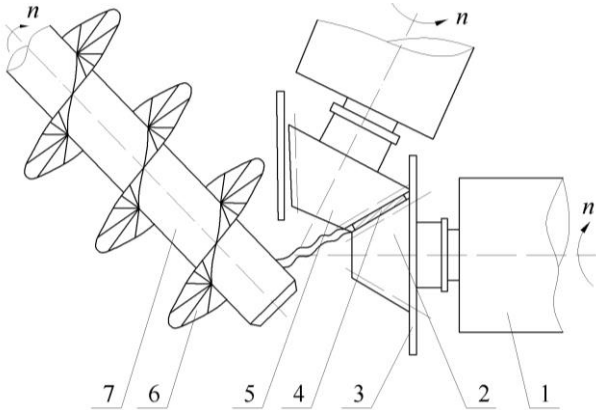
Схема формоутворення ГЗ парою неортогональних кінцевих зубчастих інструментів на обкатаному верстаті 5A725
